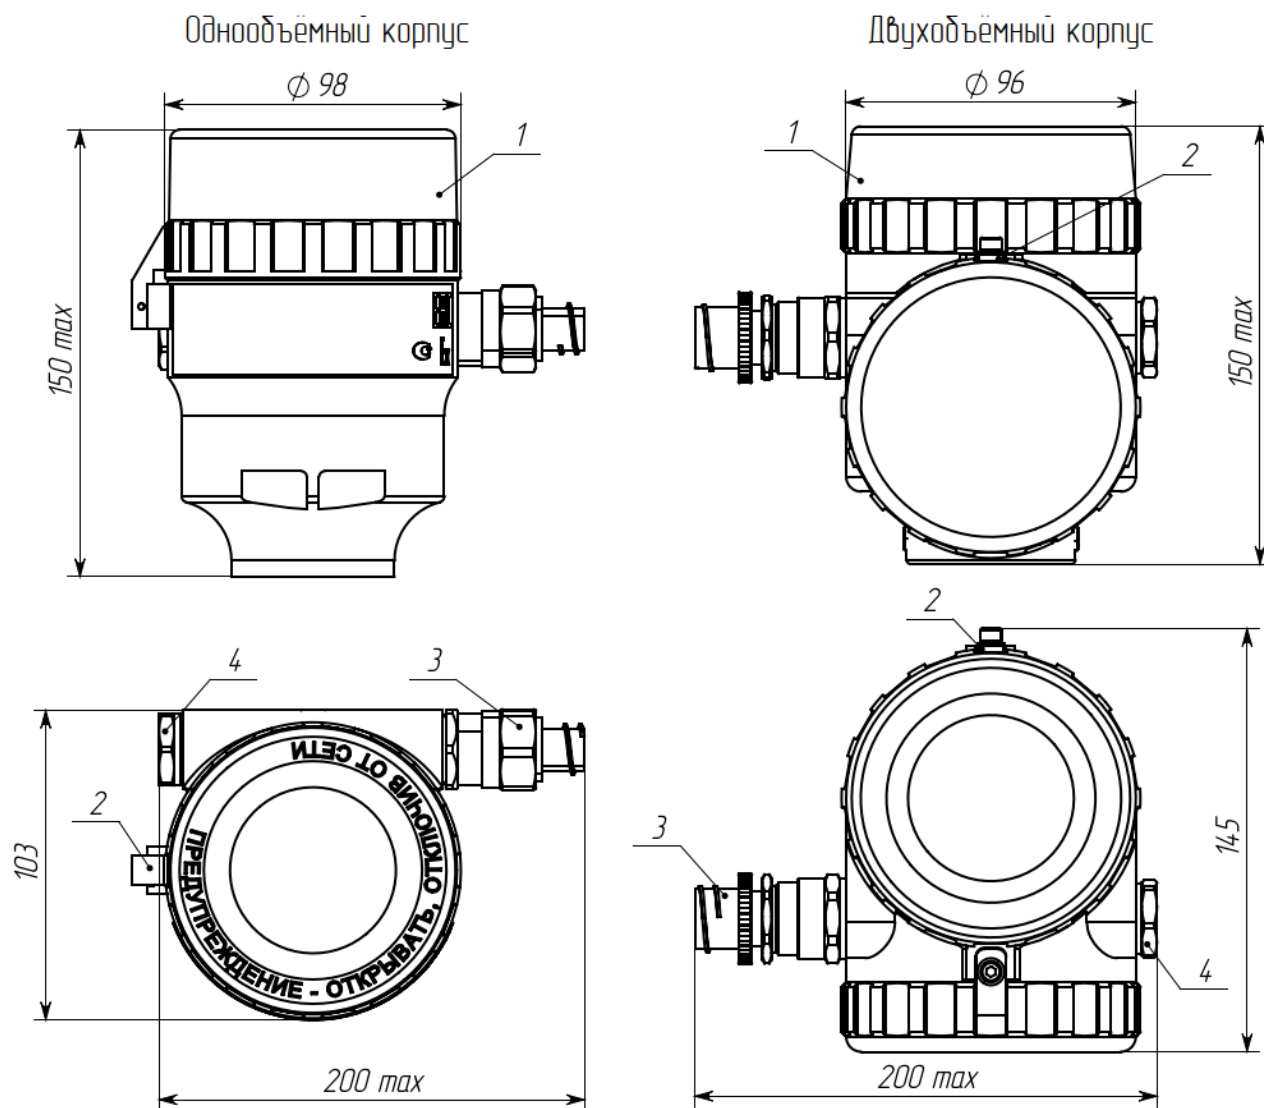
Корпус из нержавеющей стали (опция: порошково-полимерное покрытие)
